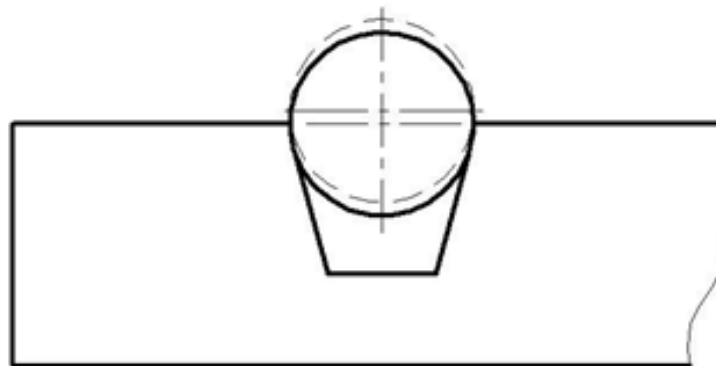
Похибка положення заготовки в захватному пристрої
